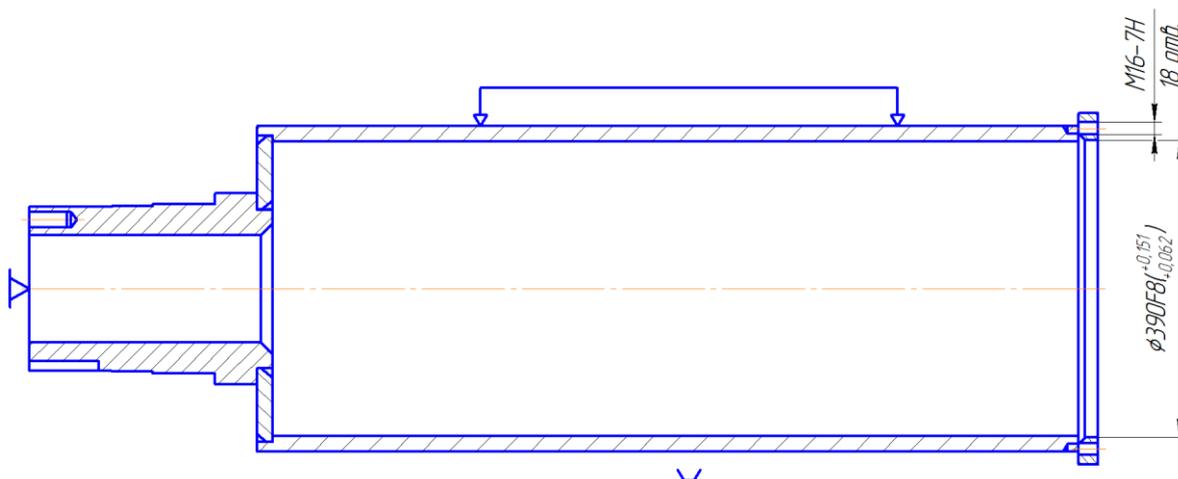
Эскиз базирования заготовки на 010 горизонтально-расточной операции.
